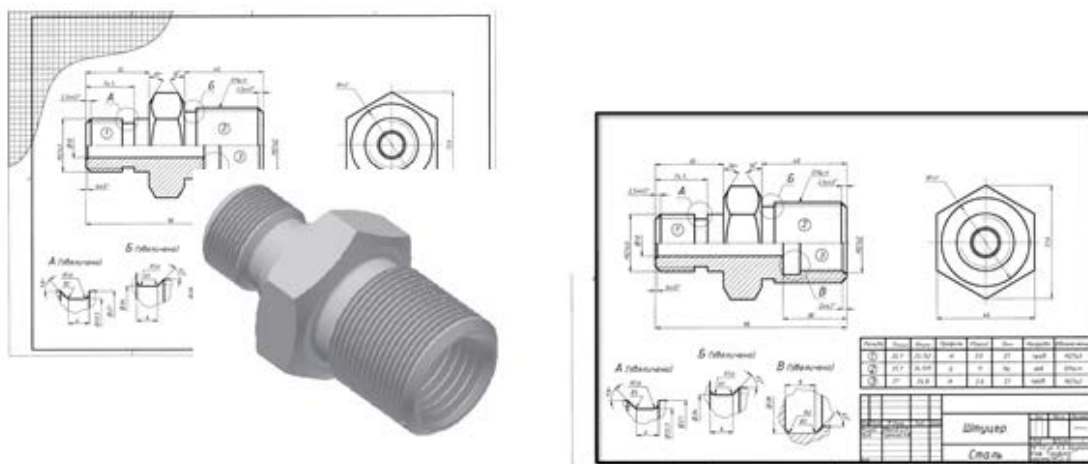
Эскиз от руки, модель и ЭЧ детали
